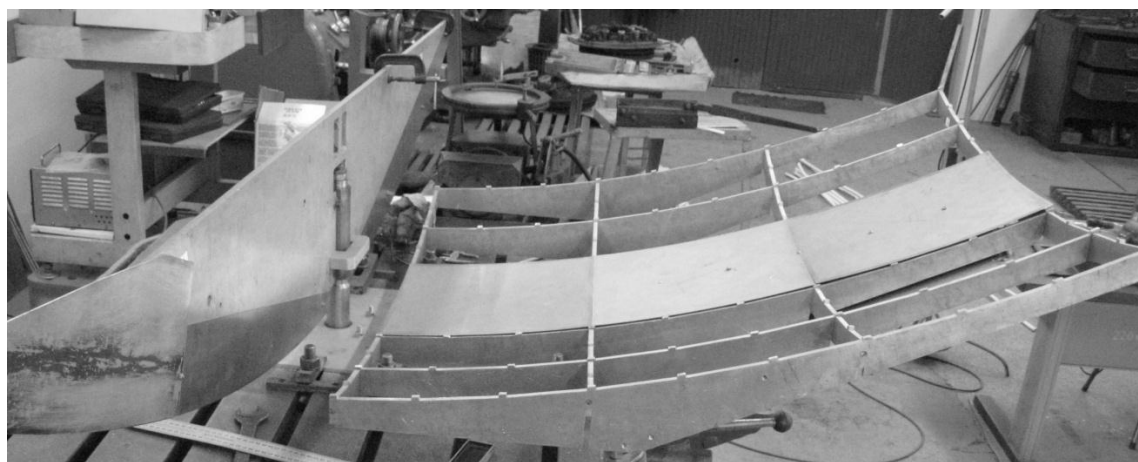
Установка для сборки зеркала: шаблон для контроля профиля зеркала (слева); металлический каркас с пластинами (справа)
